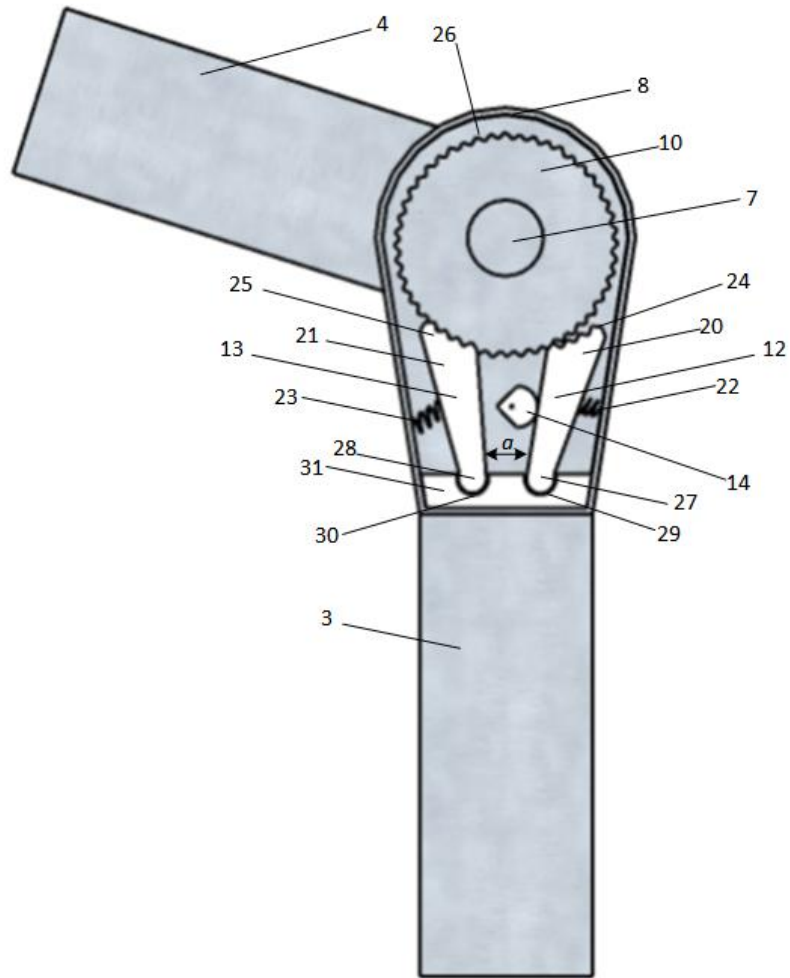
Механізм редресації верхньої кінцівки і ліктьового суглоба, кришка корпусу знята.
